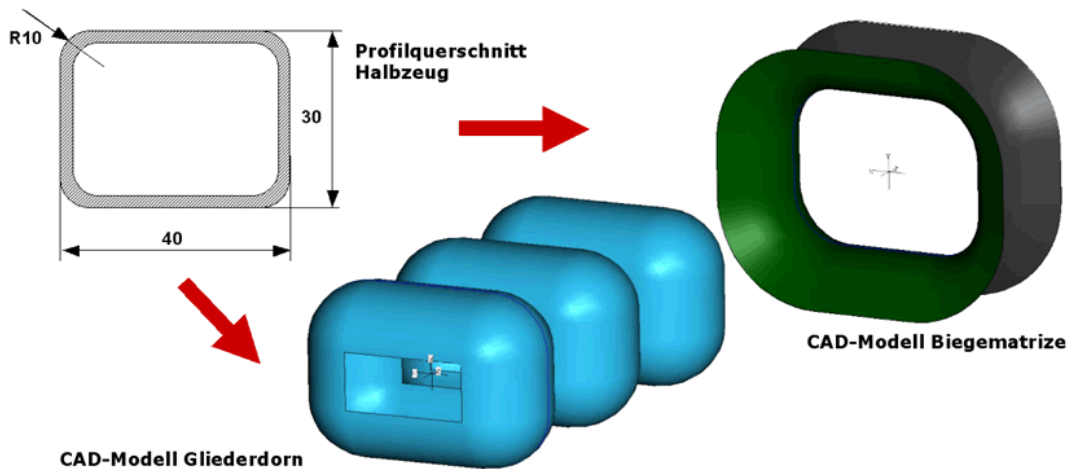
Modellierung der Biegewerkzeuge im CAD
